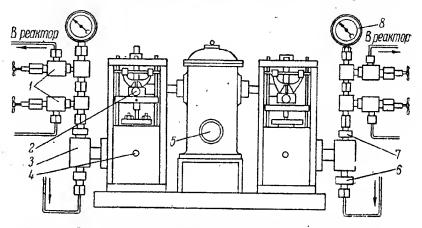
Спаренный жидкостный иасос на 500~am. 1— запориме вентили; 2— кулиса для регулировки насоса; 3— клапанная коробка; 4— цилинар; 5— редуктор; 6— всасывающий клапан; 7— нагнетательный клапан; 6— манометр.
